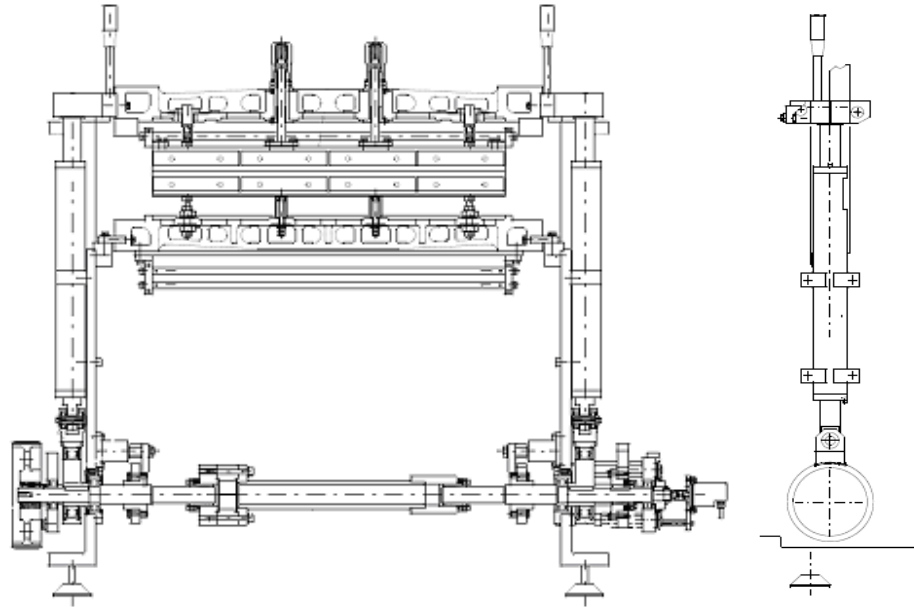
Esquema del mecanismo que mueve las barras soldadoras.
